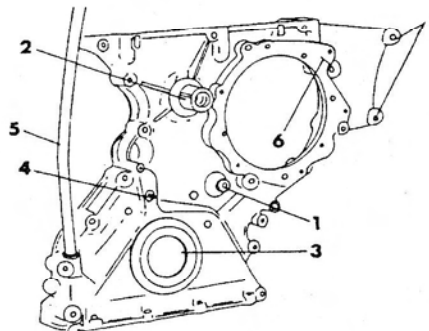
Крышка распределительного механизма и расположение различных деталей
